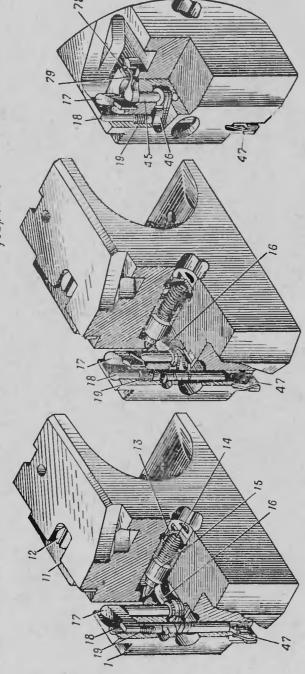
Положение деталей затвора при взведенном и спущенном ударнике: 17- ось взвод ударника: 17- ось взвода: 18- стопор извода в сборе; 19- пружина; 45- ось предохранителя спуска; 46- предохранитель спуска; 47- собачка; 78- пру-
